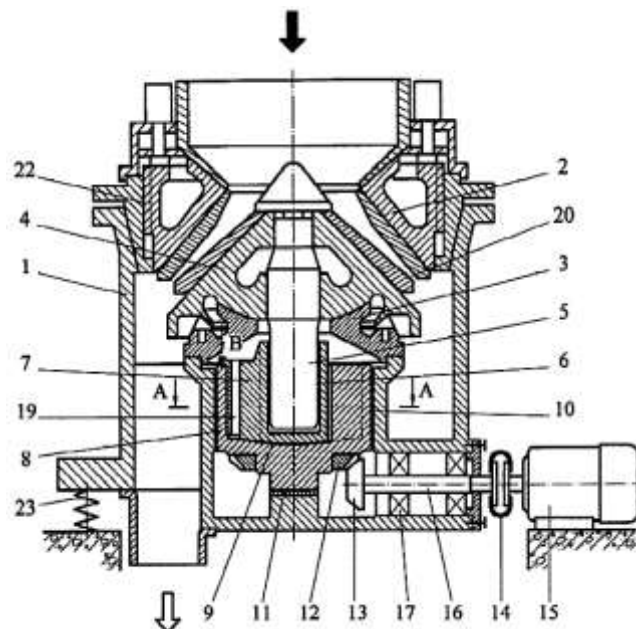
Конусная дробилка (Патент № RU91007U1)
